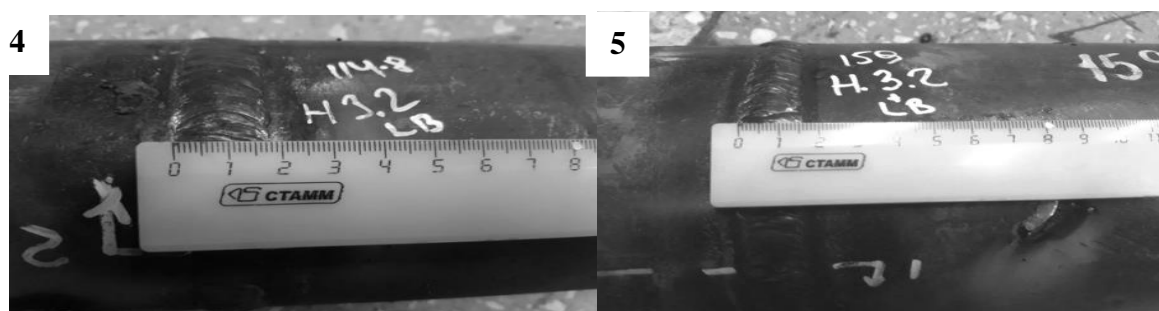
Сварное соединение 4. Рисунок Б25. Сварное соединение 5.
